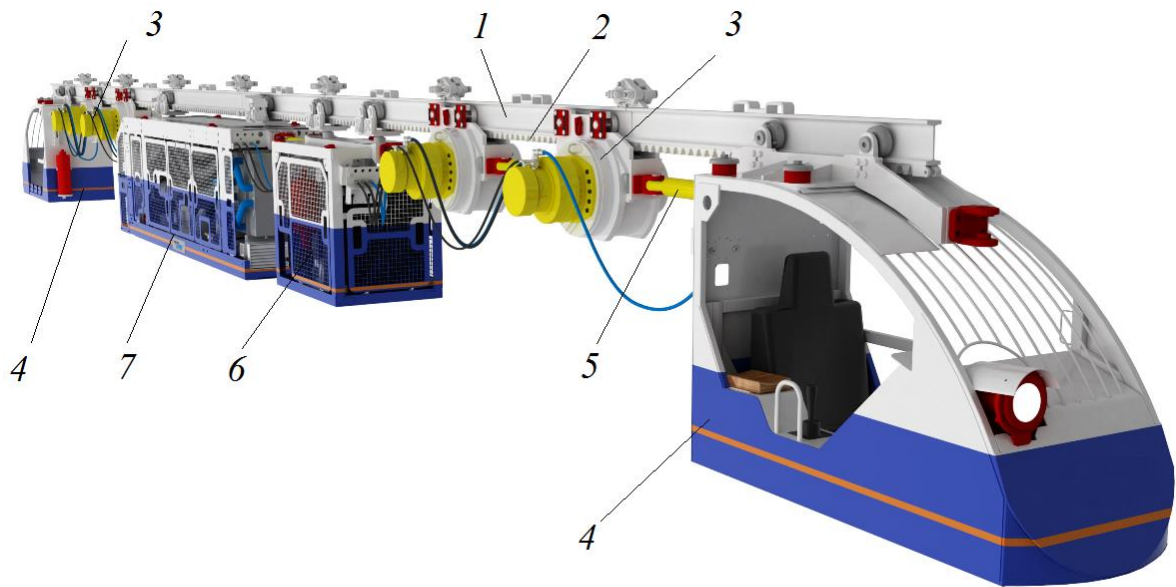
Общий вид подвесной монорельсовой дороги с зубчатым захватом BECKER KPZS-96 [297]: 1 – монорельс; 2 – зубчатая рейка; 3 – тяговое устройство; 4 – кабина управления; 5 – тяга сцепки; 6 – охладитель; 7 – дизель-гидравлический агрегат
